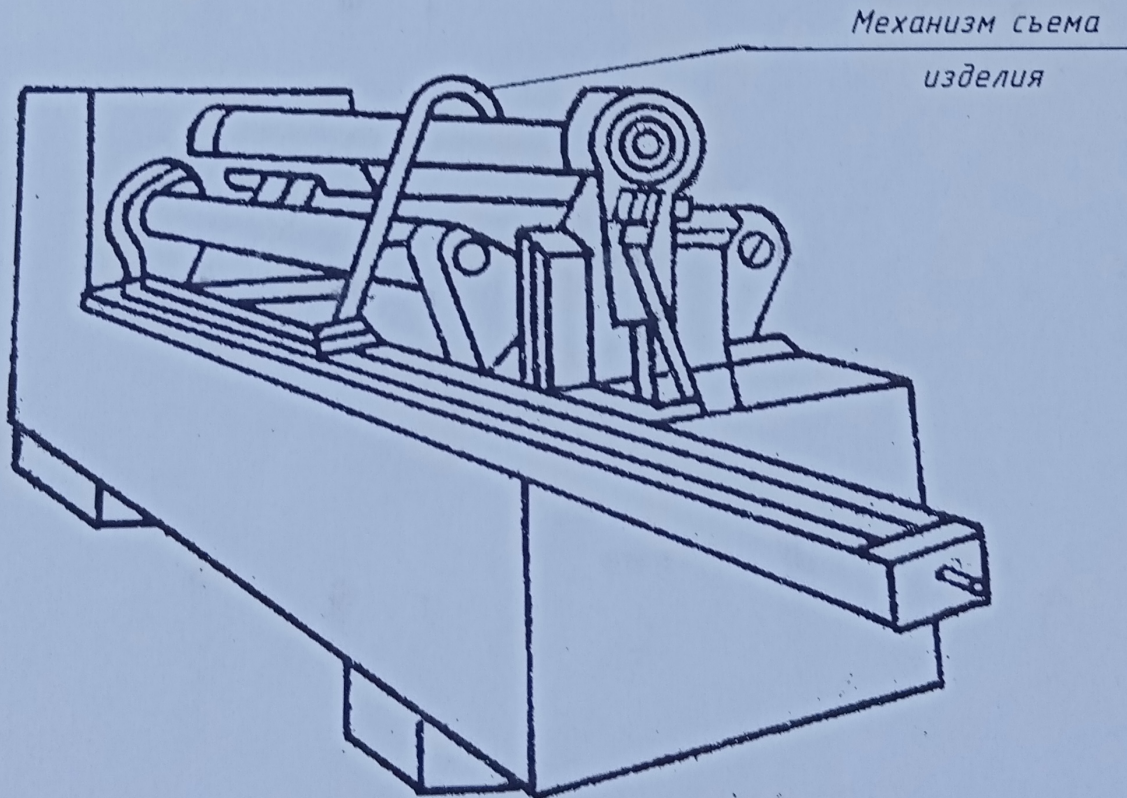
Общий вид машины листогибочной трехвалковой с механизмом съема изделий
